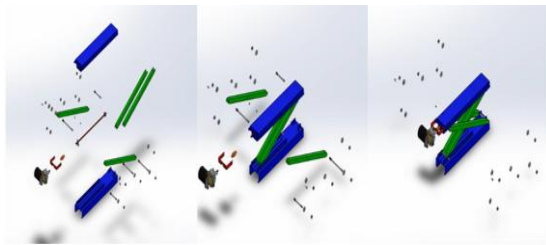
Vista explosionada del ensamblaje del gato mecánico tipo tijera motorizado desarrollada en SolidWorks. Fuente: Alfaro, Epiayu, Mora & Barros (2025).
